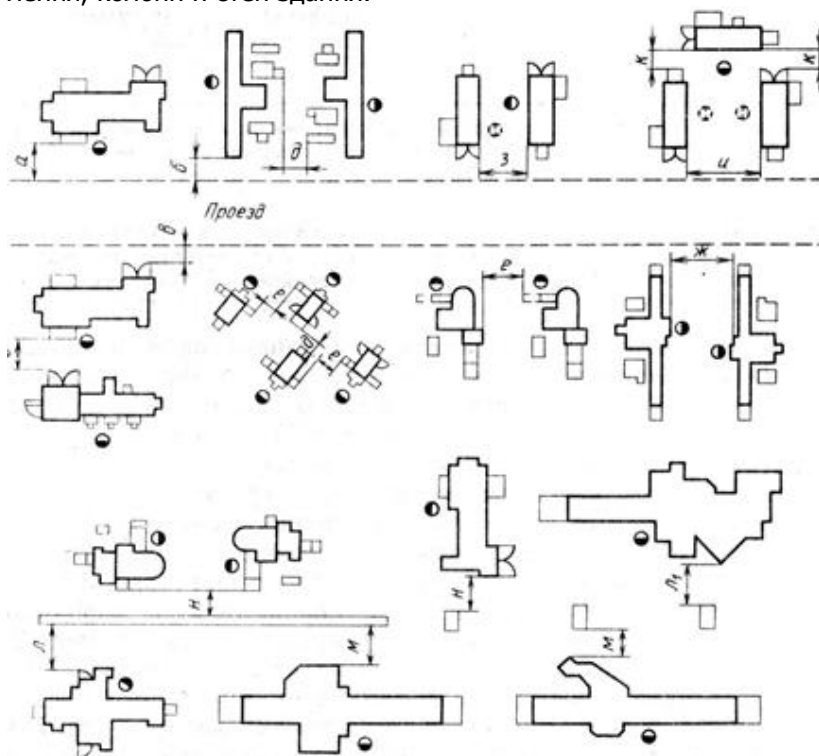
Варианты размещения станков от проезда, относительно друг друга, стен и колонн здания
